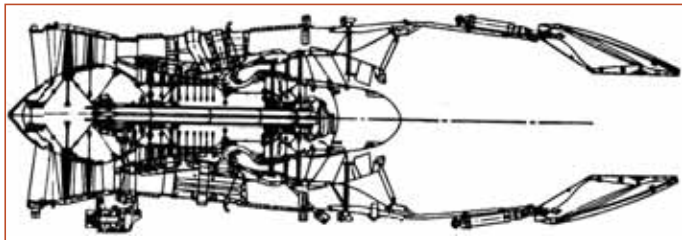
Конструктивная схема ТРДДФ F101-GE-102
